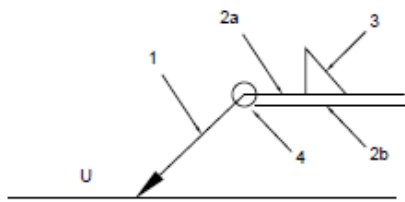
Espesor de garganta del cordón de soldadura $[a]$ [6]
